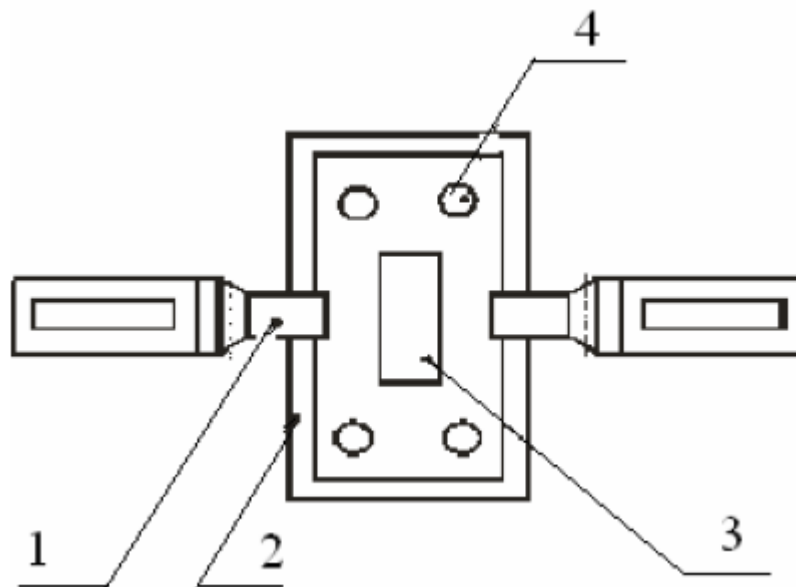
Схема ультразвукового зміцнення кульками: 1 – хвилевід; 2 – камера; 3 – оброблювана деталь; 4 – сталеві кульки.
